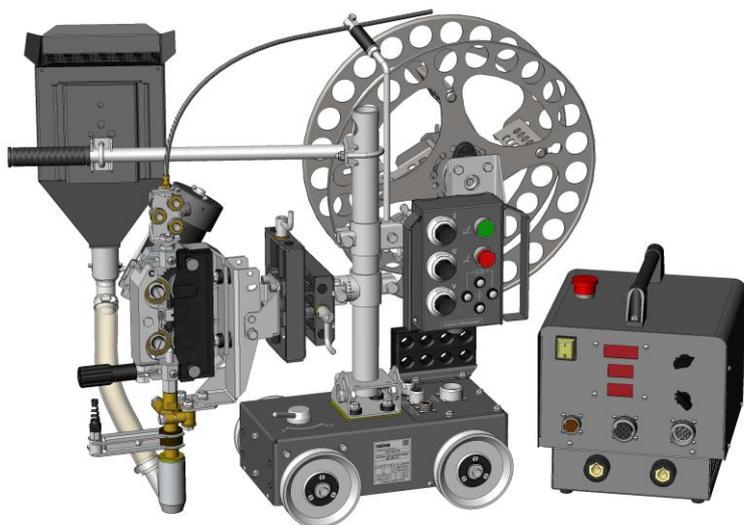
Автомат сварочный АДГ-630 исп.02
